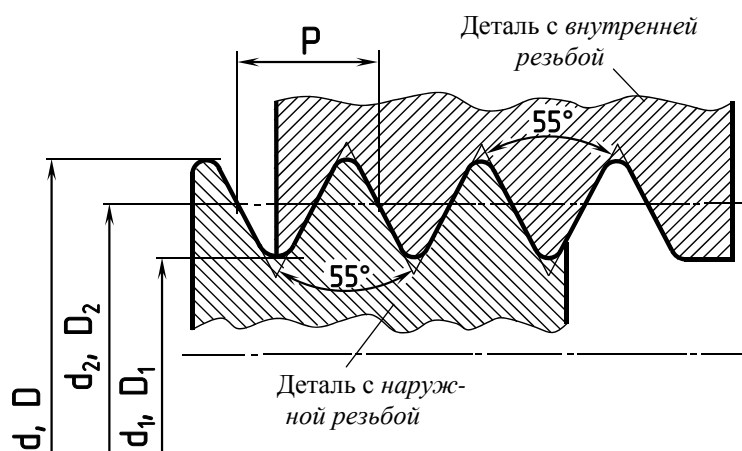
Основной профиль *трубной* резьбы: d и D – номинальные *наружные* диаметры, соответственно, наружной и внутренней резьбы; d_1 и D_1 – номинальные *внутренние* диаметры этих резьб; d_2 и D_2 – их средние диаметры; P – шаг резьбы
